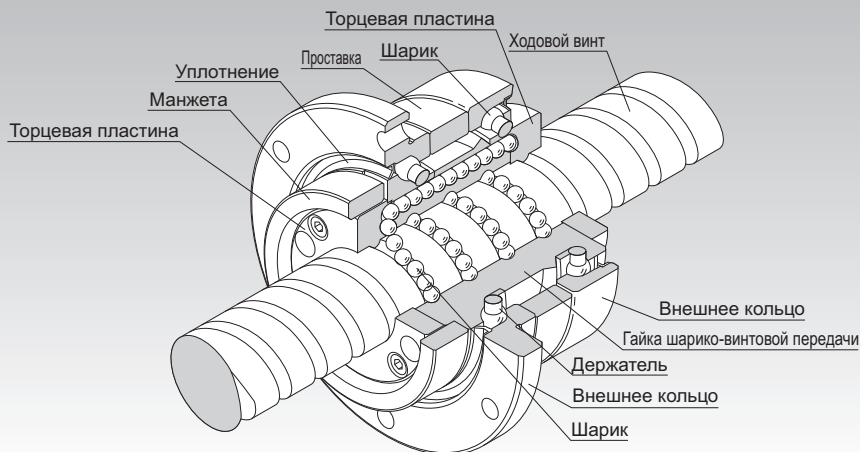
Конструкция шарико-винтовой передачи с поворотной гайкой и большим шагом резьбы модели BLR
